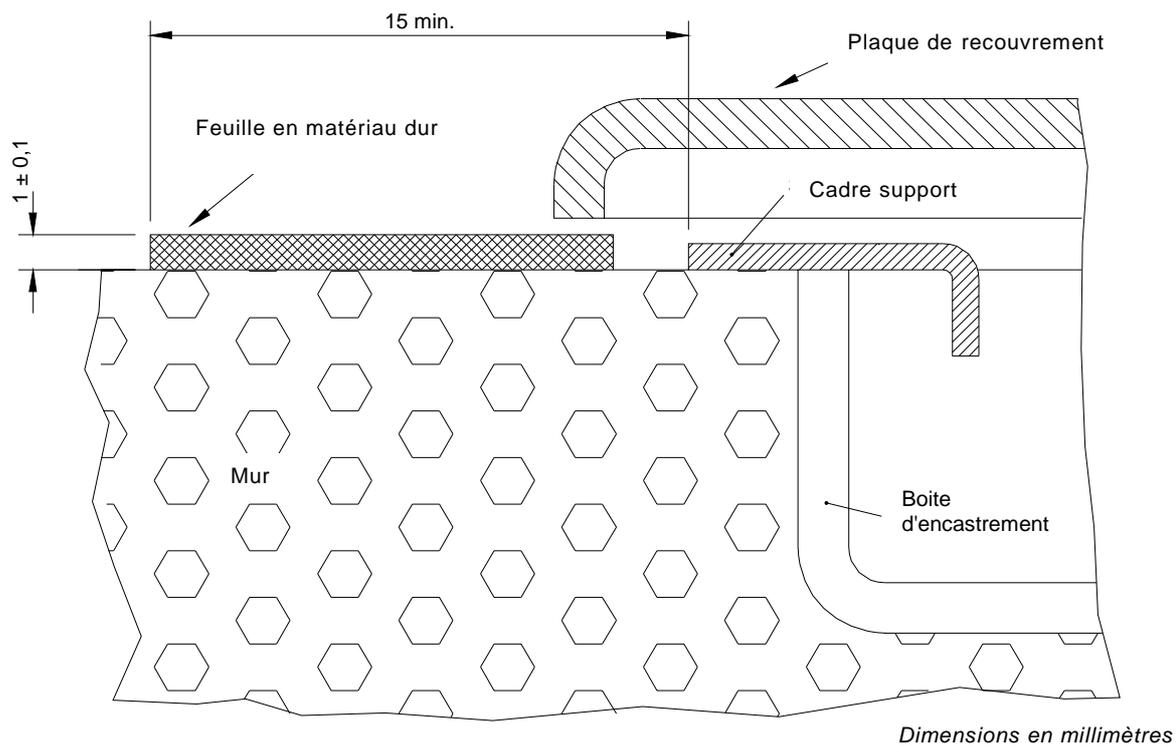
Disposition pour l'essai des capots ou des plaques de recouvrement
